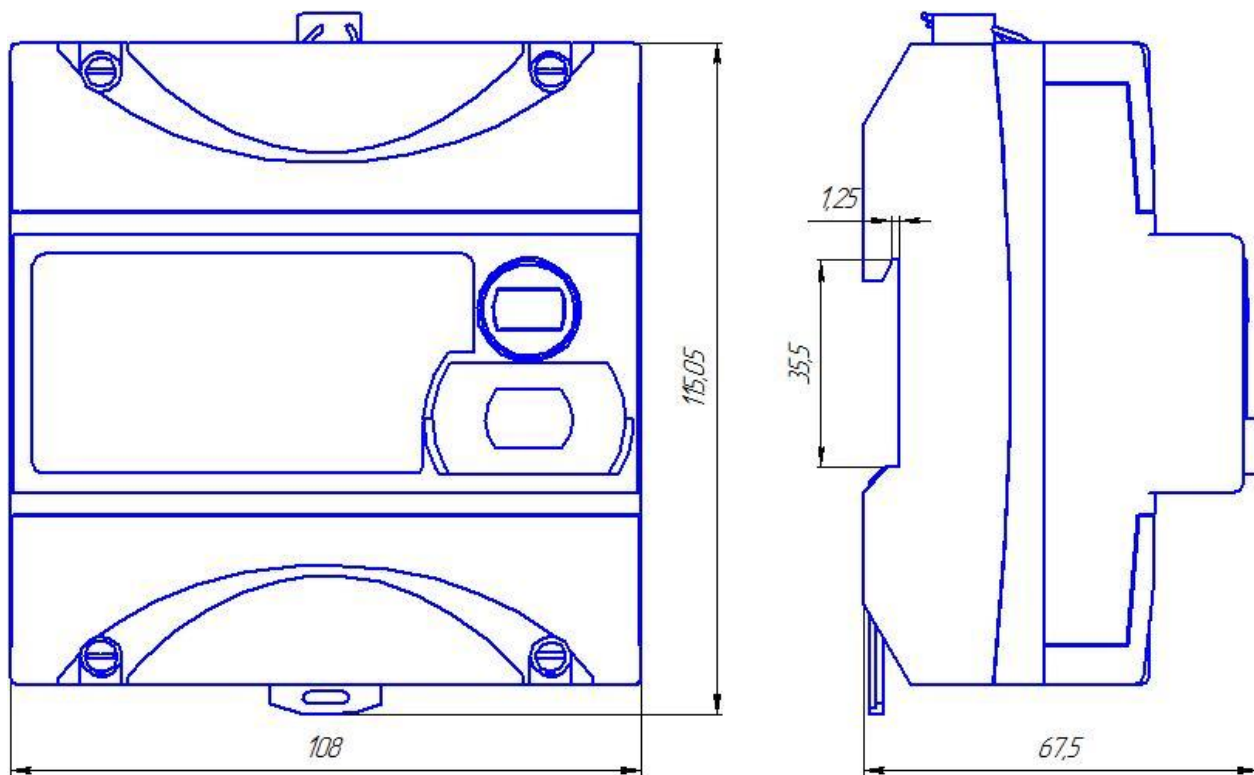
Габаритный чертеж и установочные размеры терминала
